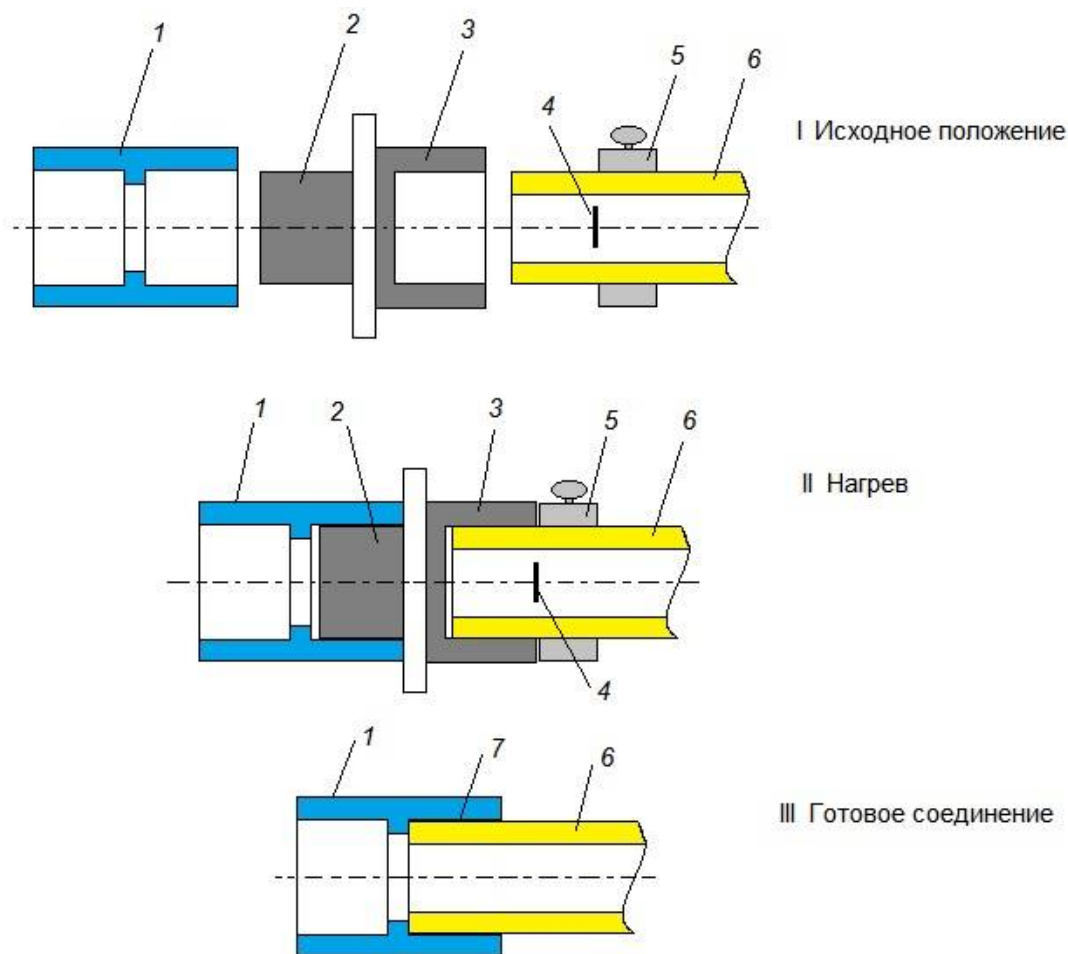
Последовательность процесса контактной сварки в раструб трубы и муфты из PPRC.
